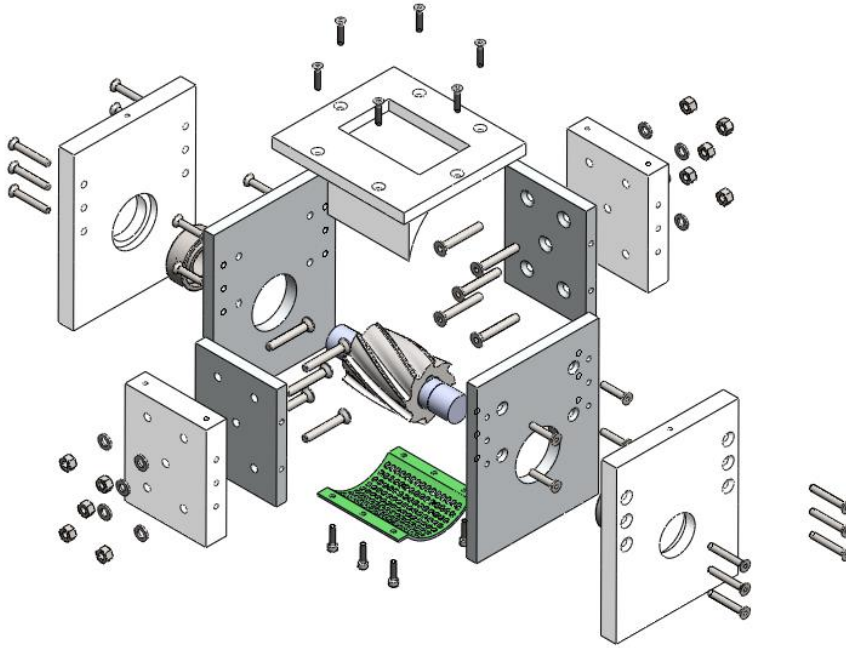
Conjunto explosionado (detalle rejilla de corte) [Fuente propia]
